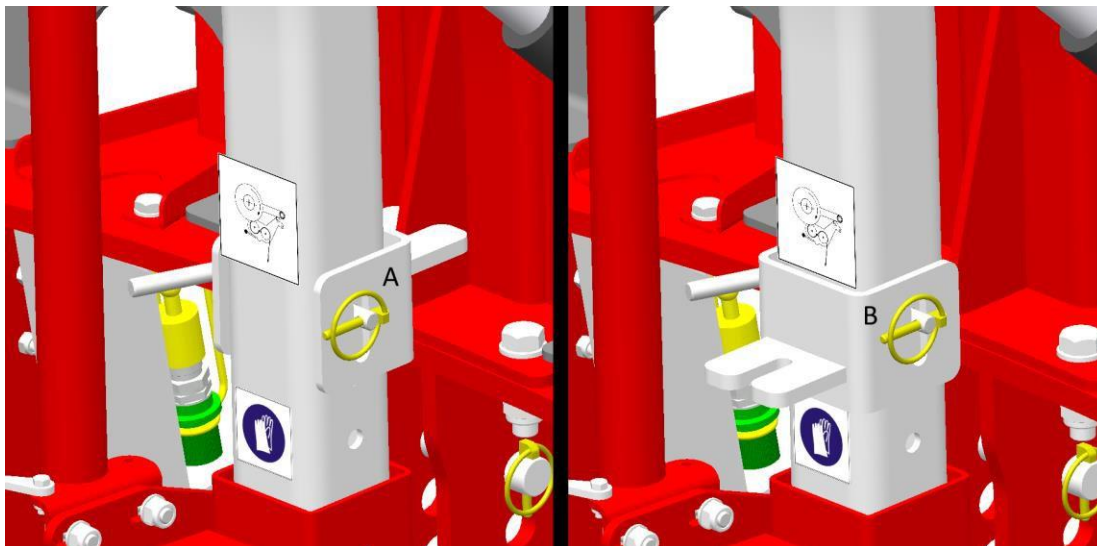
Транспортный рычаг обматывающего рычага: А - положение заблокировано; В - разблокированное положение
